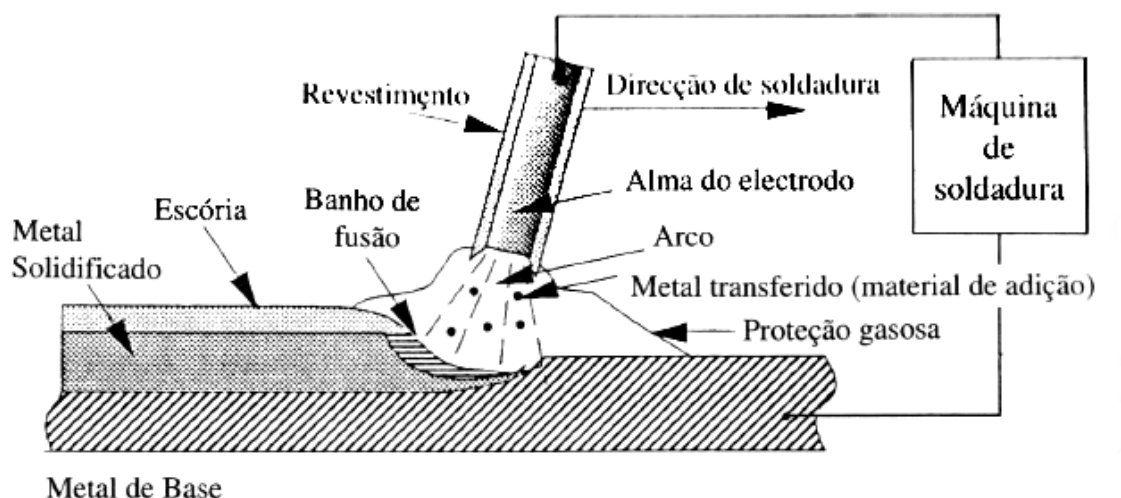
Soldadura com eléctrodos revestidos[1]
